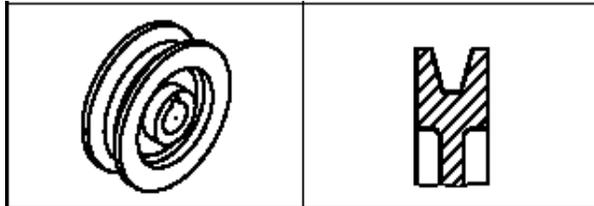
Polia com canal trapezoidal ou em “V”, simples.
